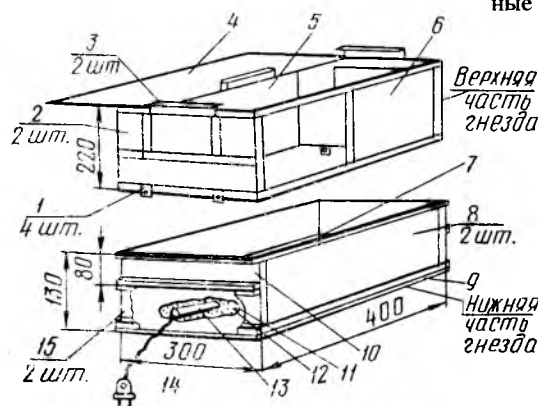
Разборное гнездо: 1 — пластина соединительная; 2 — стенка боковая верхней части гнезда; 3 — направляющая; 4 — крышка гнезда; 5 — стенка задняя; 6 — стенка передняя; 7 — пол; 8 — стенка фронтальная; 9 — крышка поддона нижняя; 10 — стенка боковая нижней части гнезда; 11 — полиэтиленовый пакет; 12 — песок; 13 — трубка; 14 — электрошнур; 15 — крышка поддона боковая
